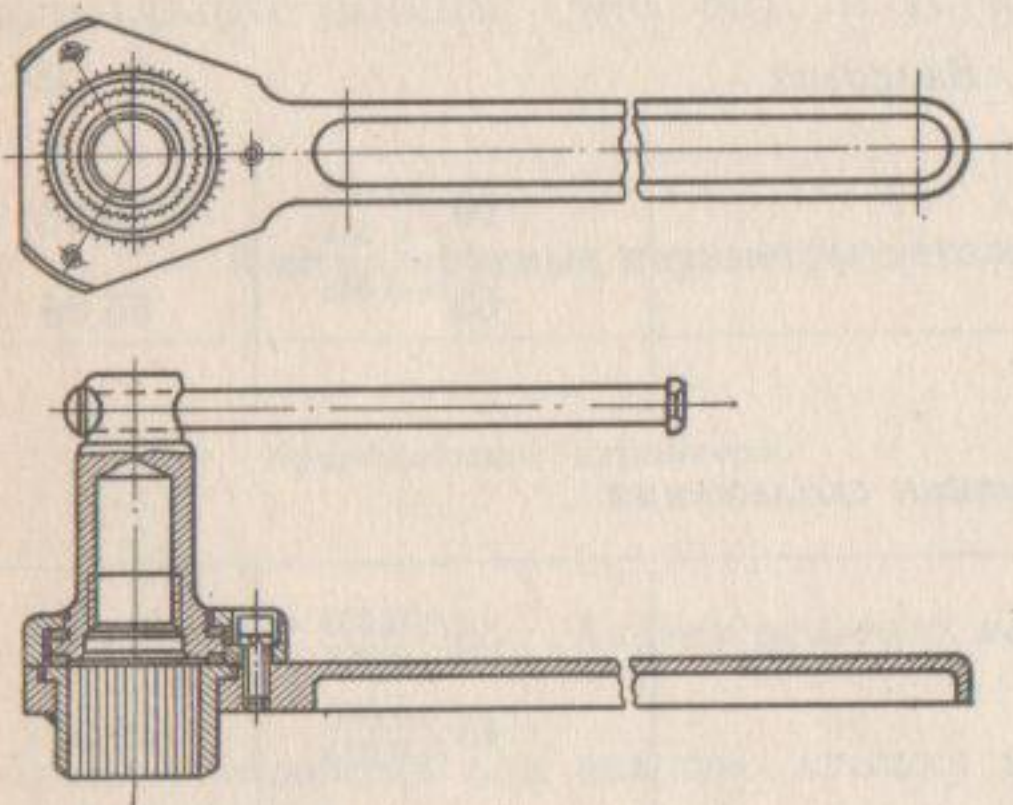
Общий вид рычажного ключа для поворота вала сошки
